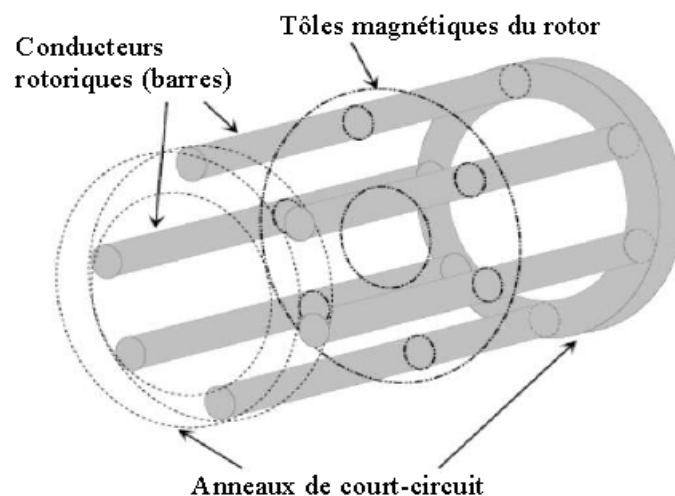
Vue schématique en perspective du rotor à cage d'écureuil [6].
